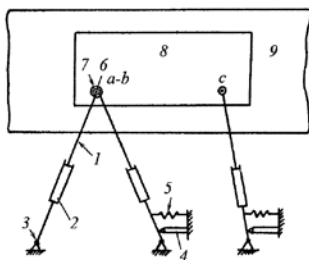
1 – координатный манипулятор с двумя захватами
